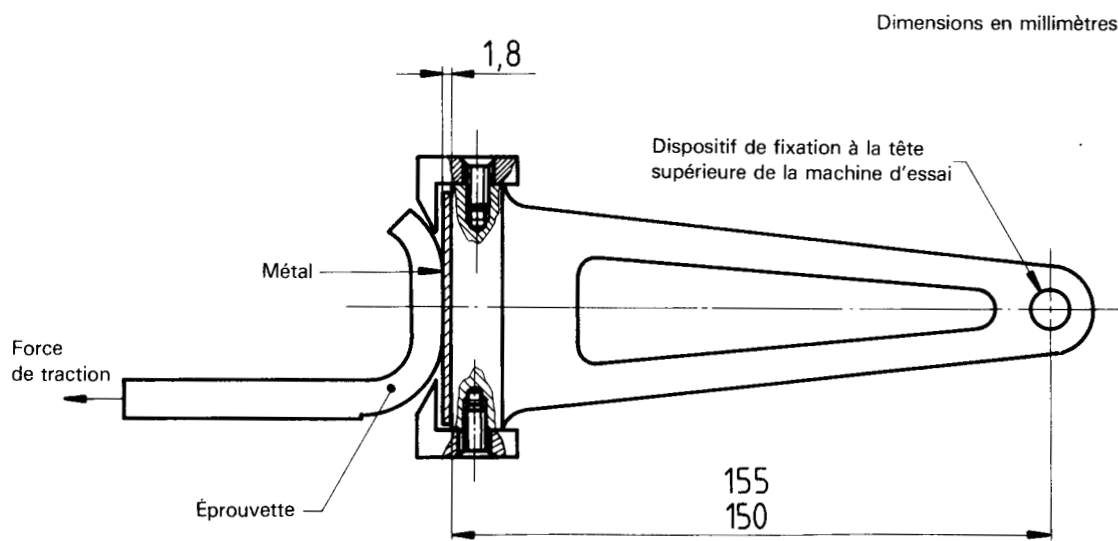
Exemple de dispositif de fixation pour l'essai d'adhérence
